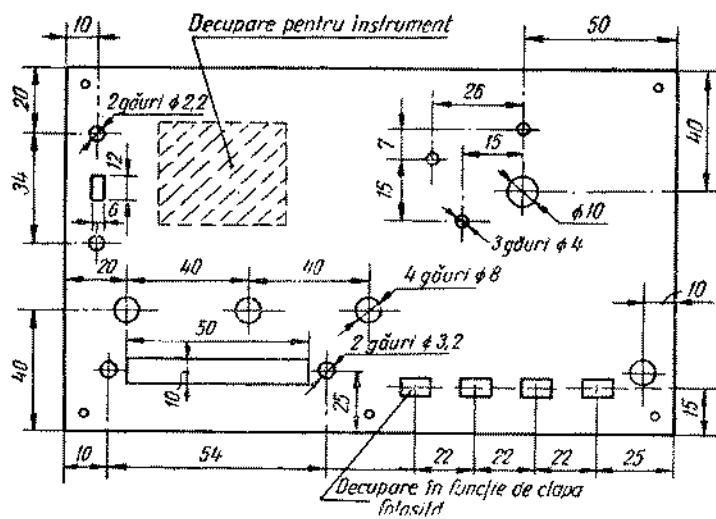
Panou frontal. Dimensiunile decupărilor.
